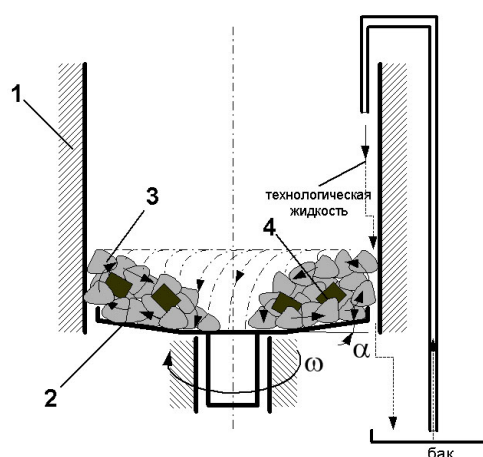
Схема процесса ЦРО: 1 – обечайка рабочей камеры; 2 – вращающееся дно ротора; 3 – абразивный наполнитель; 4 – обрабатываемые детали
